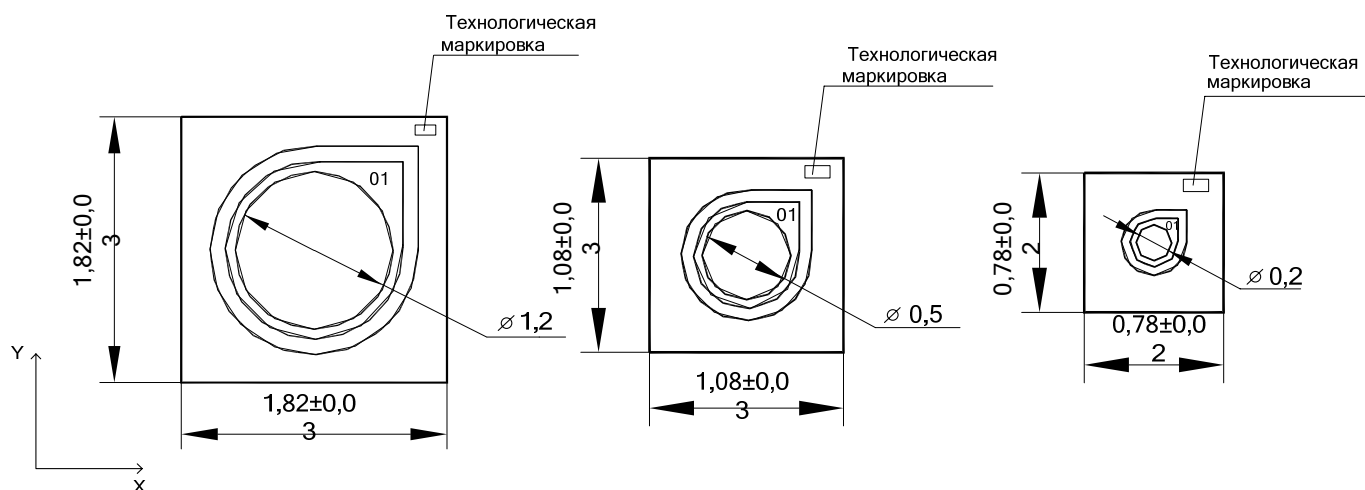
Габаритные размеры корпуса КТ-1-2
